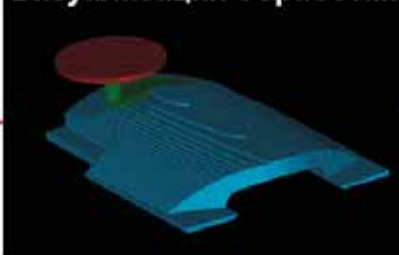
Основа изготовления изделия – конструкторская 3D-модель
